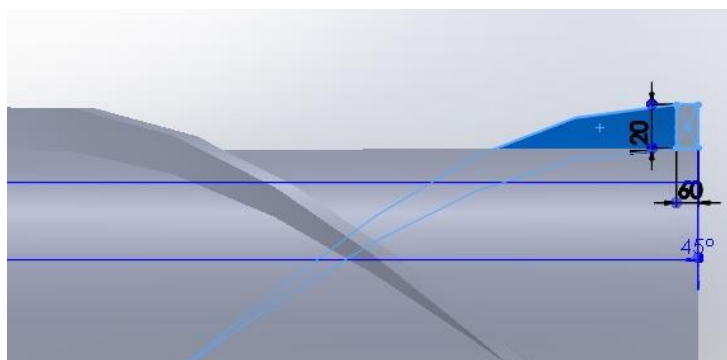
Torre e dimensões mínimas – secção de cintas [mm]
